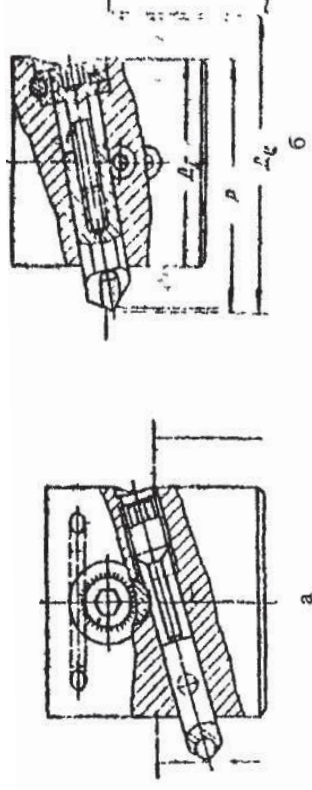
Установка для расточки с использованием оправки с шариком (а) и установка резца (б)
